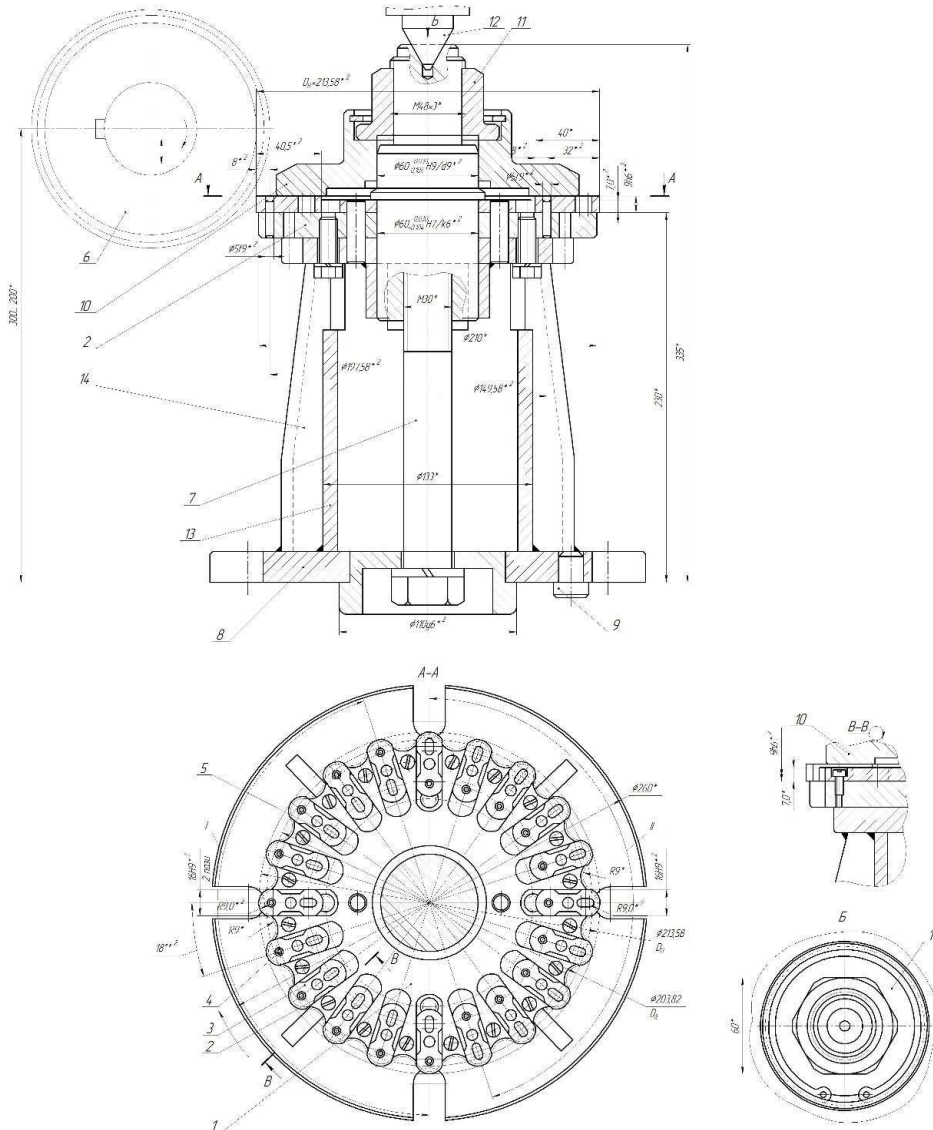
пристрій для виготовлення гальмівних елементів приводів машин на зубофрезерному верстаті
